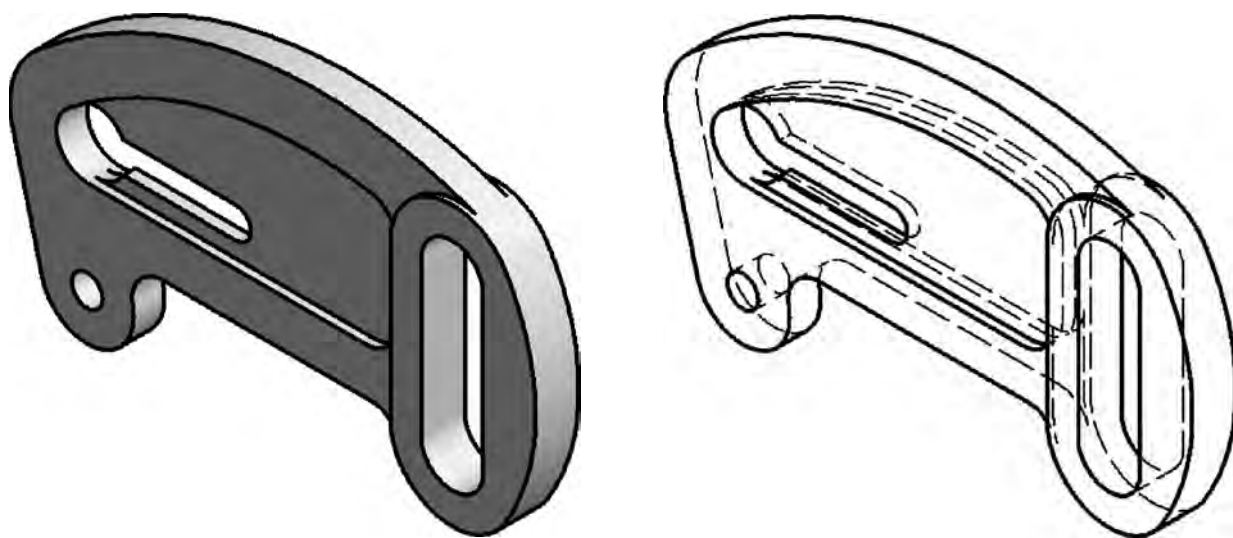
Деталь, содержащая сопряжения поверхностей (к чертежу на рис. 2.2)
